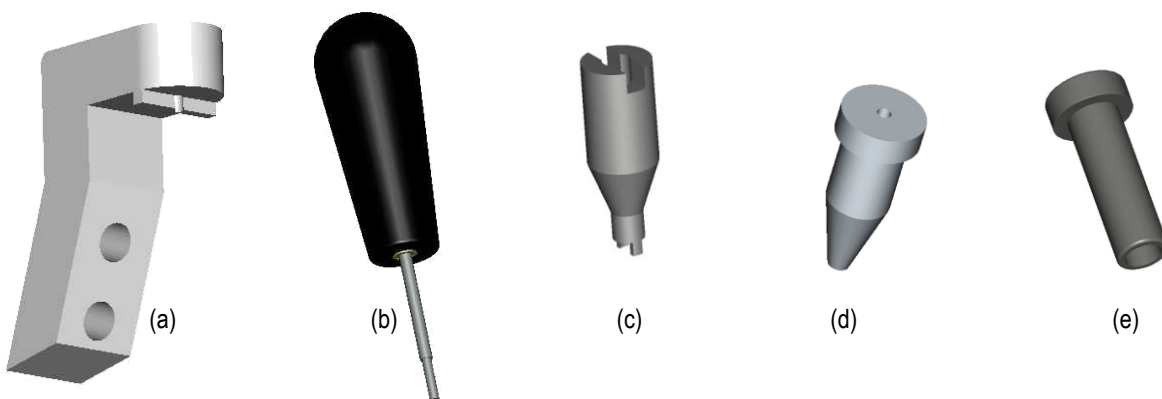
Piezas que conforman el segundo prototipo de la herramienta: a) mango direccional, b) mango de inserción, c) conector entre el clavo y la herramienta, d) guía cilíndrica de la broca, e) guía cilíndrica del destornillador.
